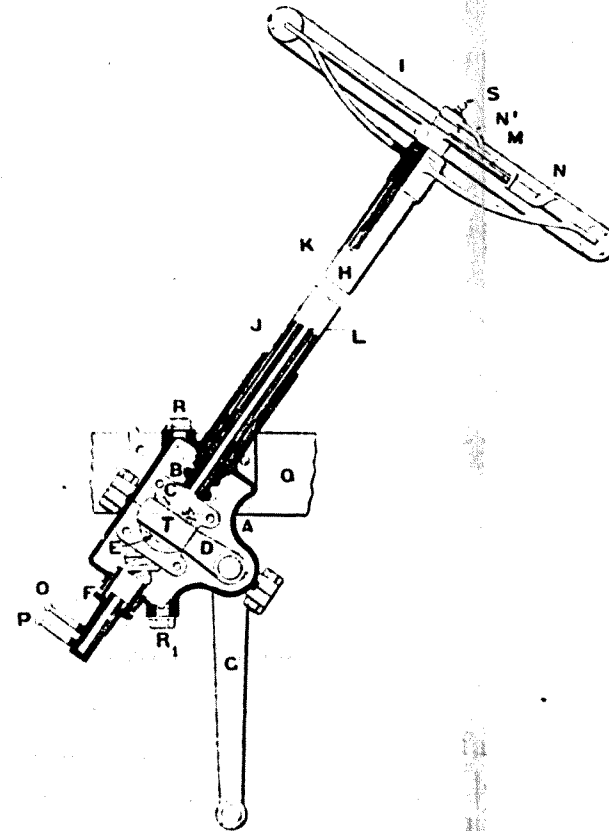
Direction à vis et écrou en deux pièces, avec rotules.
